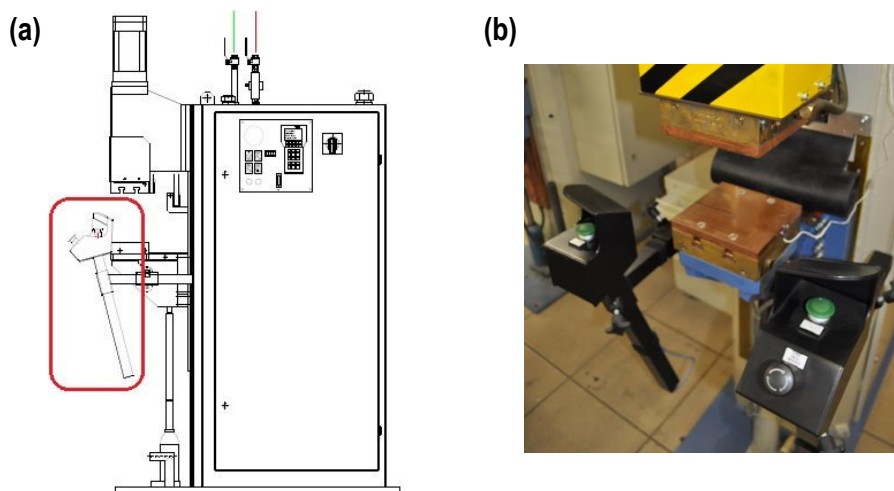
a) Ubicación y b) detalle de los dispositivos de marcha de la máquina de soldadura.
